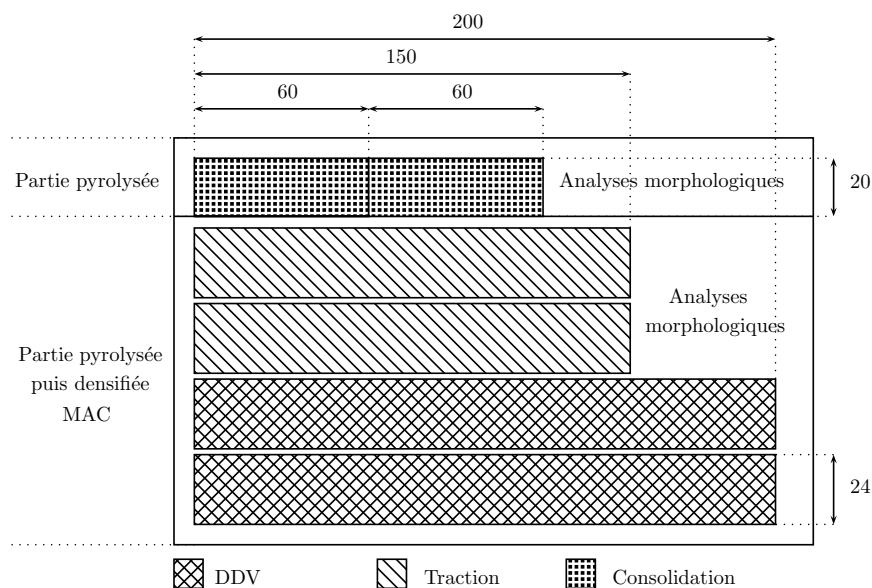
Plan de découpe des éprouvettes des matériaux C(CVL)/MAC.
